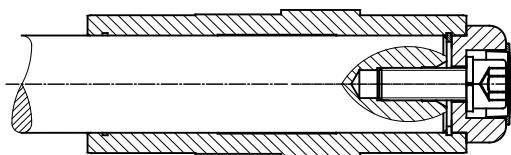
Установка редуктора на вал без буртика с помощью крепежного элемента
